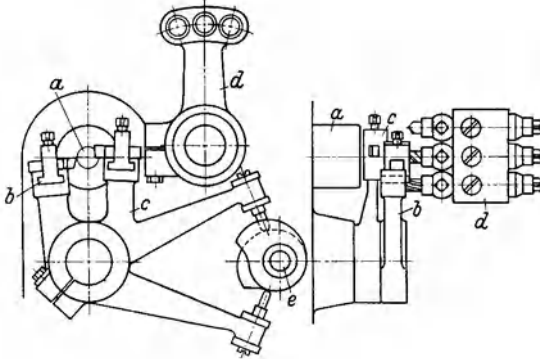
Schema des Arbeitsraumes eines Formautomaten mit schwingendem Werkzeugträger für drei Bohrwerkzeuge (Klein u. Ungerer).
